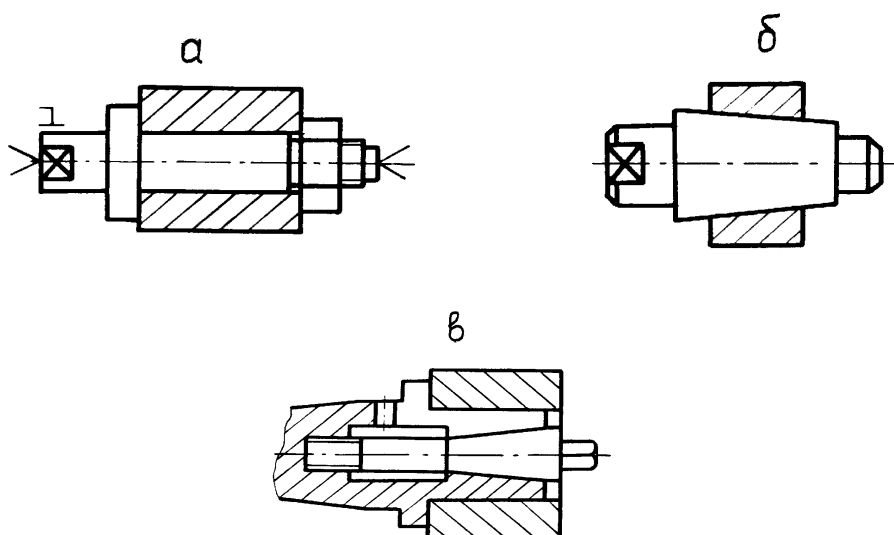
Оправки: а — цилиндрическая; б — коническая; в — цанговая
